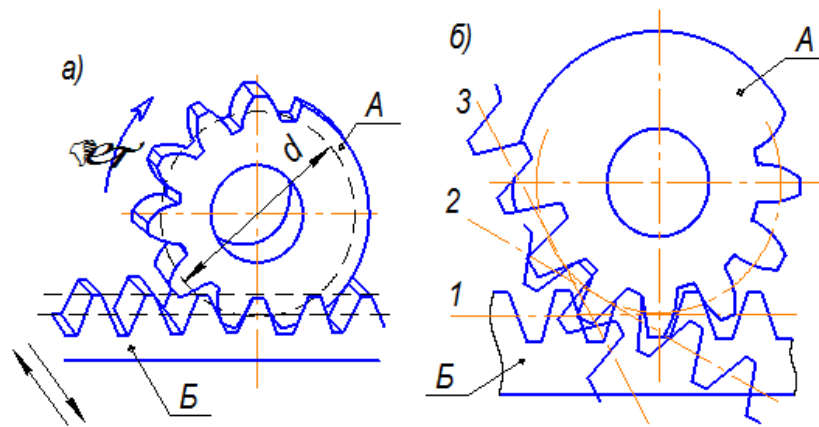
Нарезание зубьев методом обкатки: а – схема процесса нарезания зубьев; б – схема образования профиля зуба
